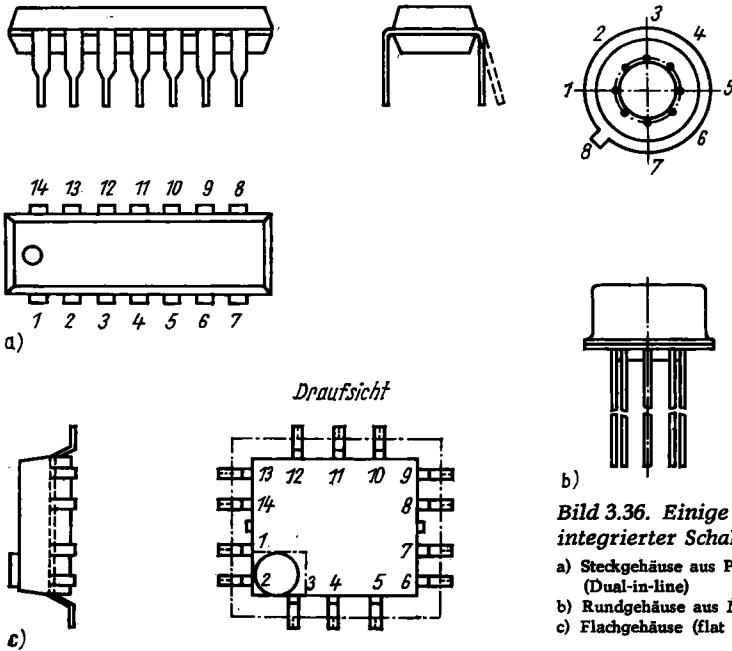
Einige Gehäuseformen integrierter Schaltkreise
